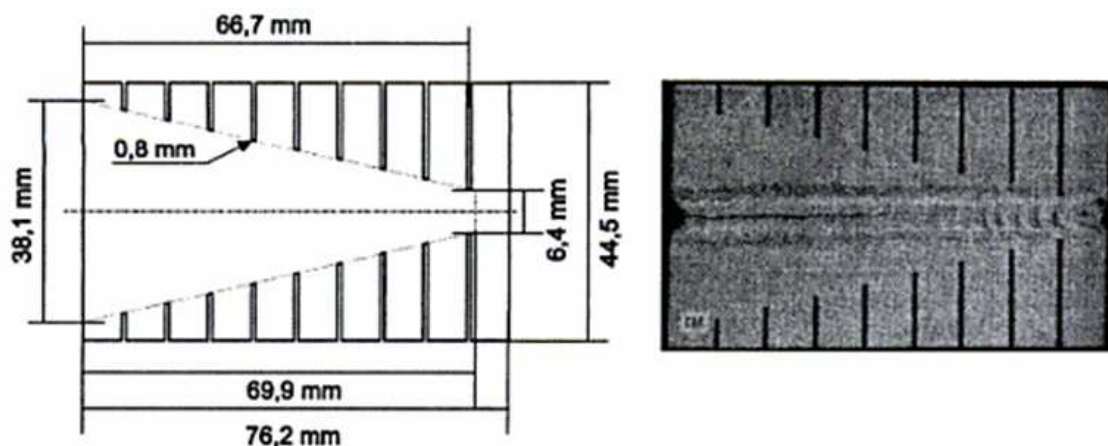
Houldcraft Probe. links: Abmessung (WIG Verfahren) rechts: Schweißergebnis mit einem Heißriss in der Nahtmitte [26]
